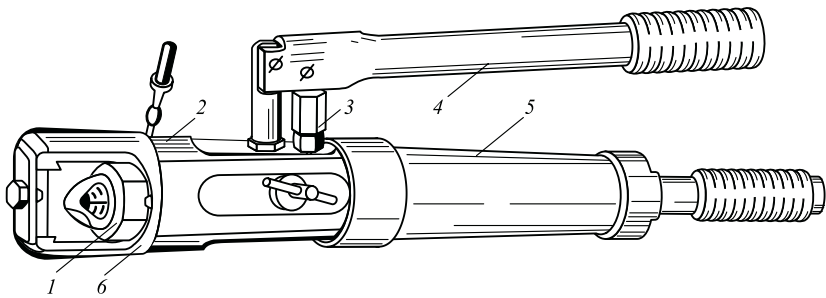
Ручной гидравлический пресс РГП-7:
